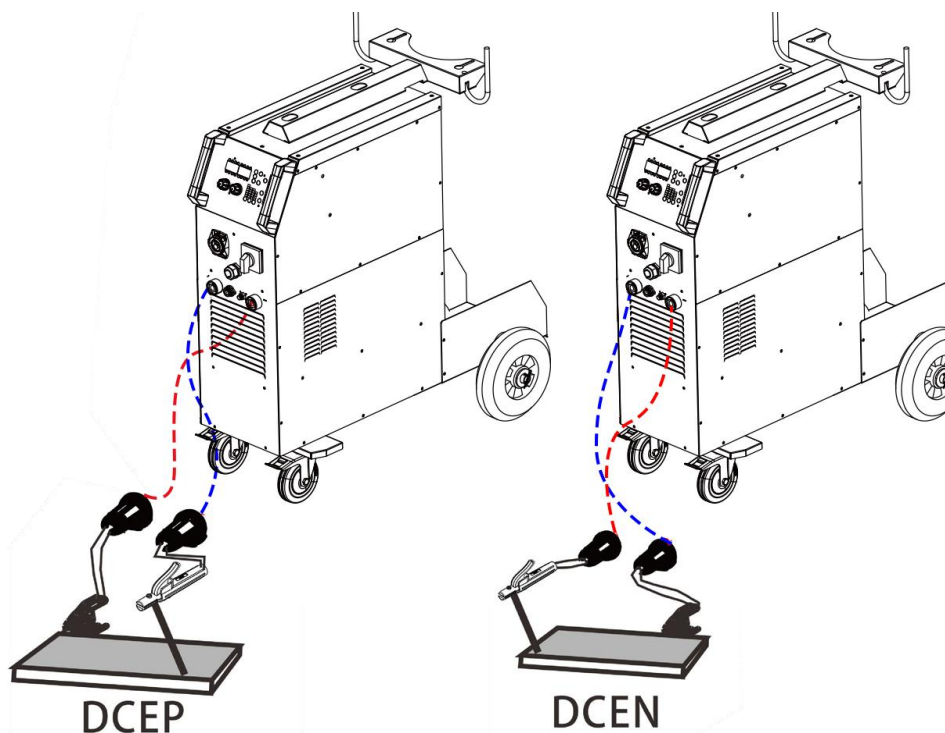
Conexão DCEP e DCEN do para soldagem com eletrodo revestido.
